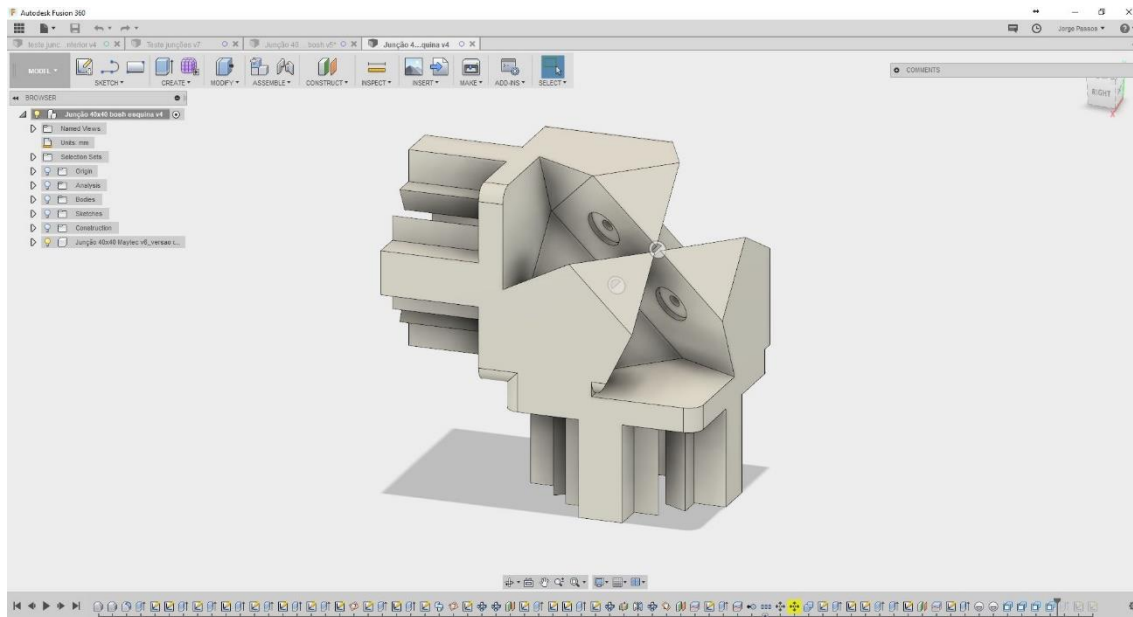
Adaptação do sistema de união, aplicando mais um eixo construtivo. Imagem: Jorge Passos
